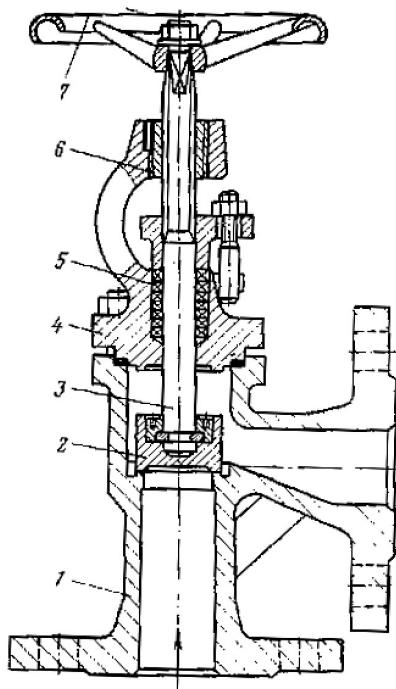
Угловой запорный вентиль: 1 — корпус; 2 — золотник; 3 — шпиндель; 4 — крышка; 5 — сальник; 6 — ходовая гайка; 7 — маховик
